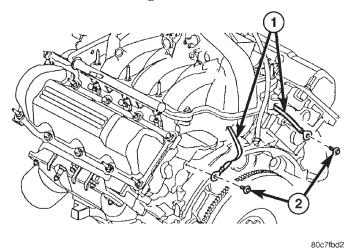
TIRA DE MASA A MOTOR - 3.7L
